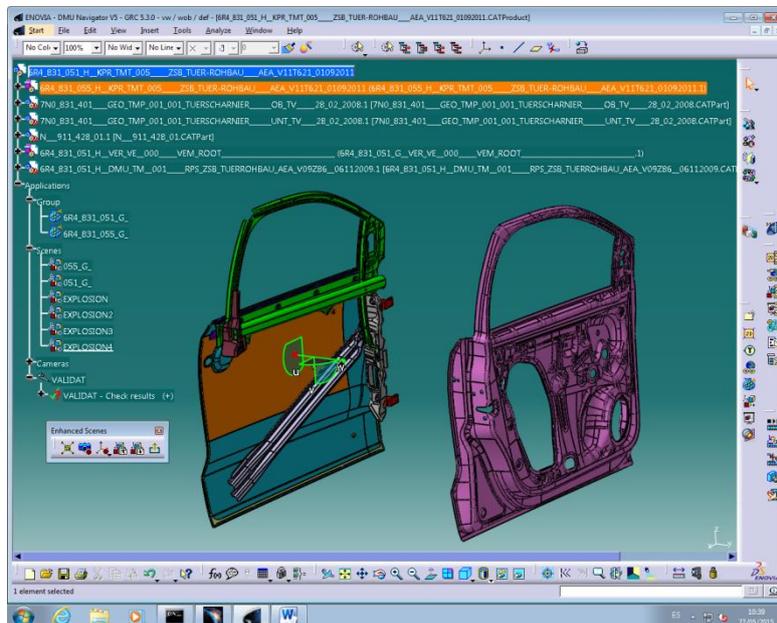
Explosionado por partes del conjunto puerta anterior izquierda en DMU
